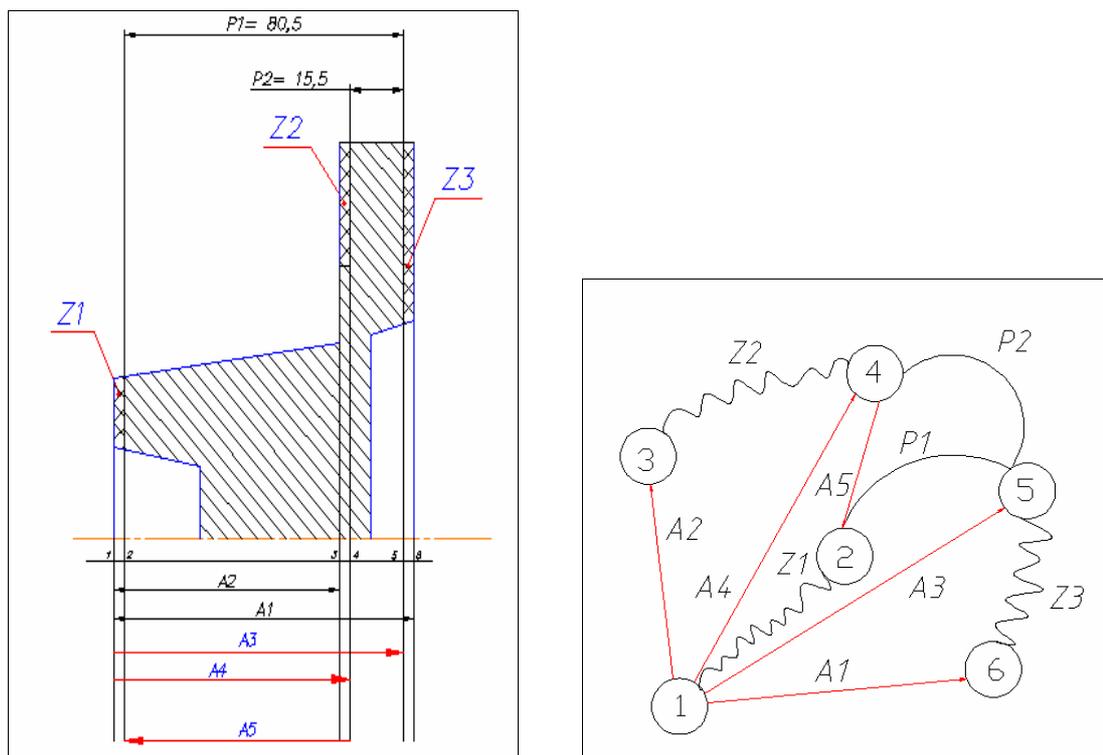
Размерная схема и граф размерных изменений заготовки
